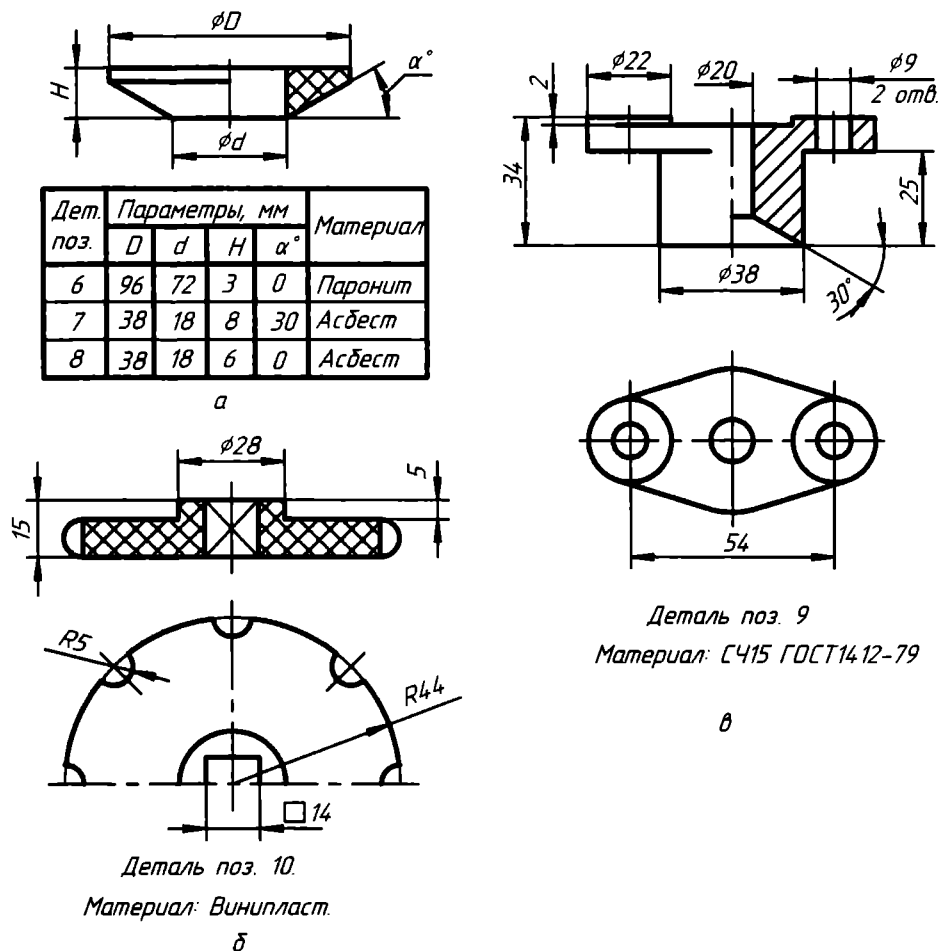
Чертежи: а — уплотнительных колец; б — маховика; в — фланца
